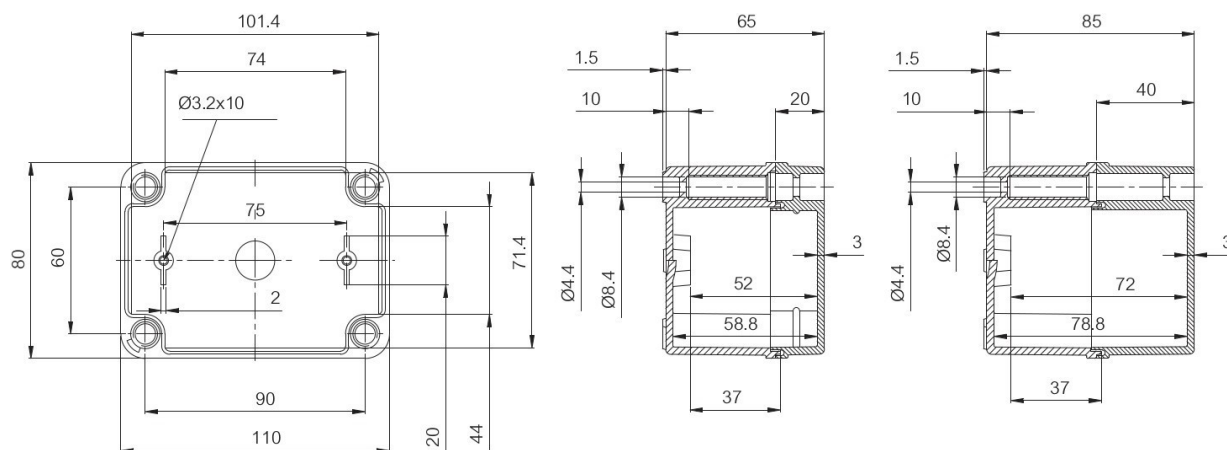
Gehäuseabmessungen (in mm). Hinweis: Zeichnung ohne Kabelverschraubung und Sensor.
